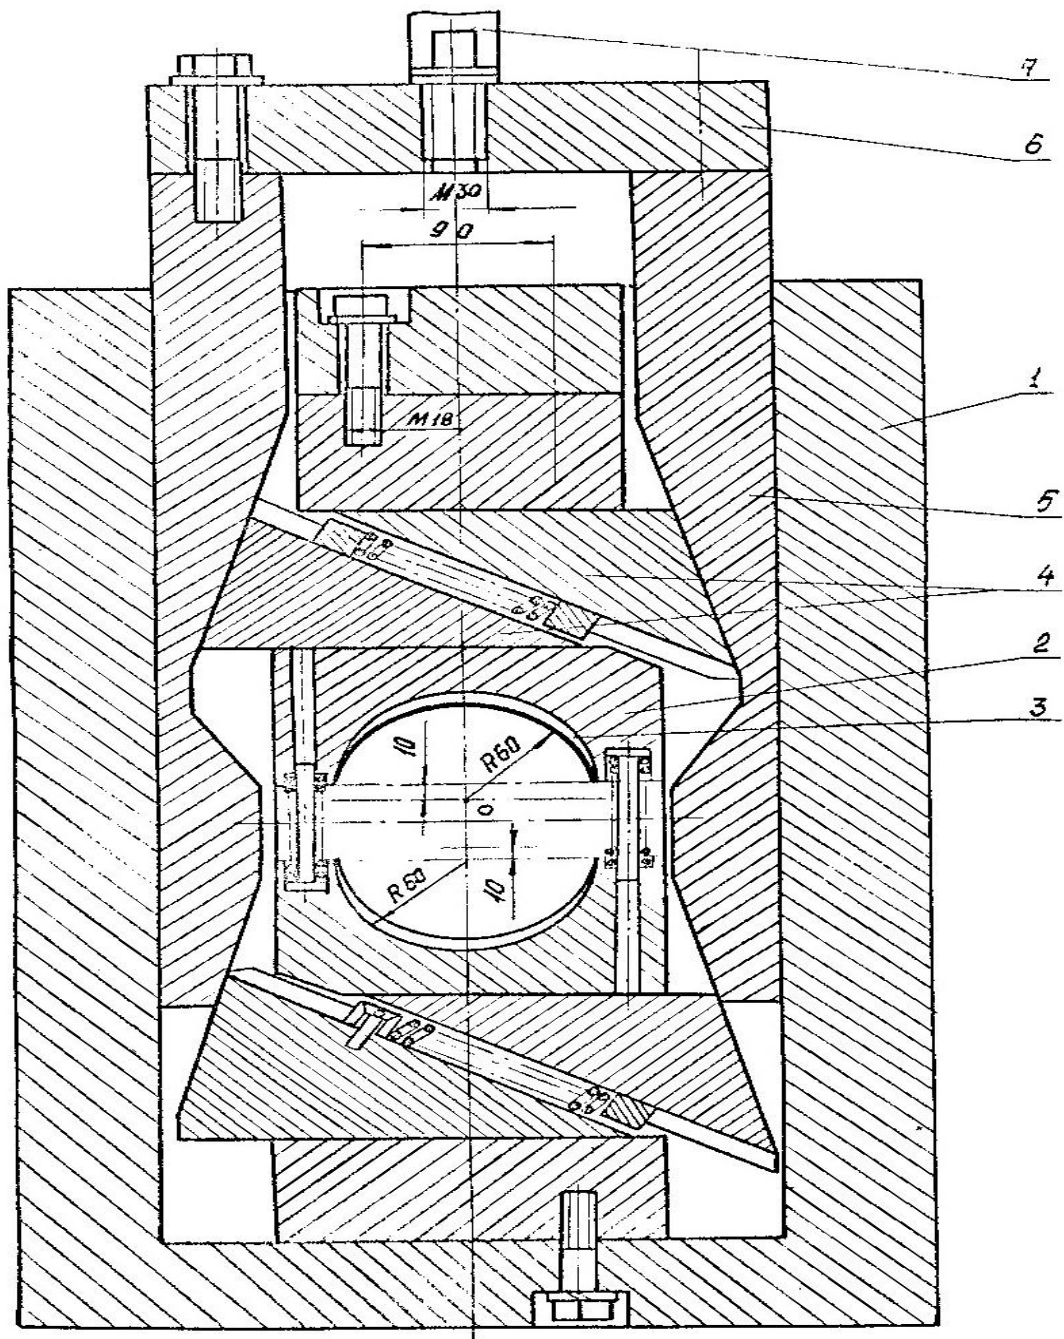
Поперечний розріз штампa для різання кола O125
